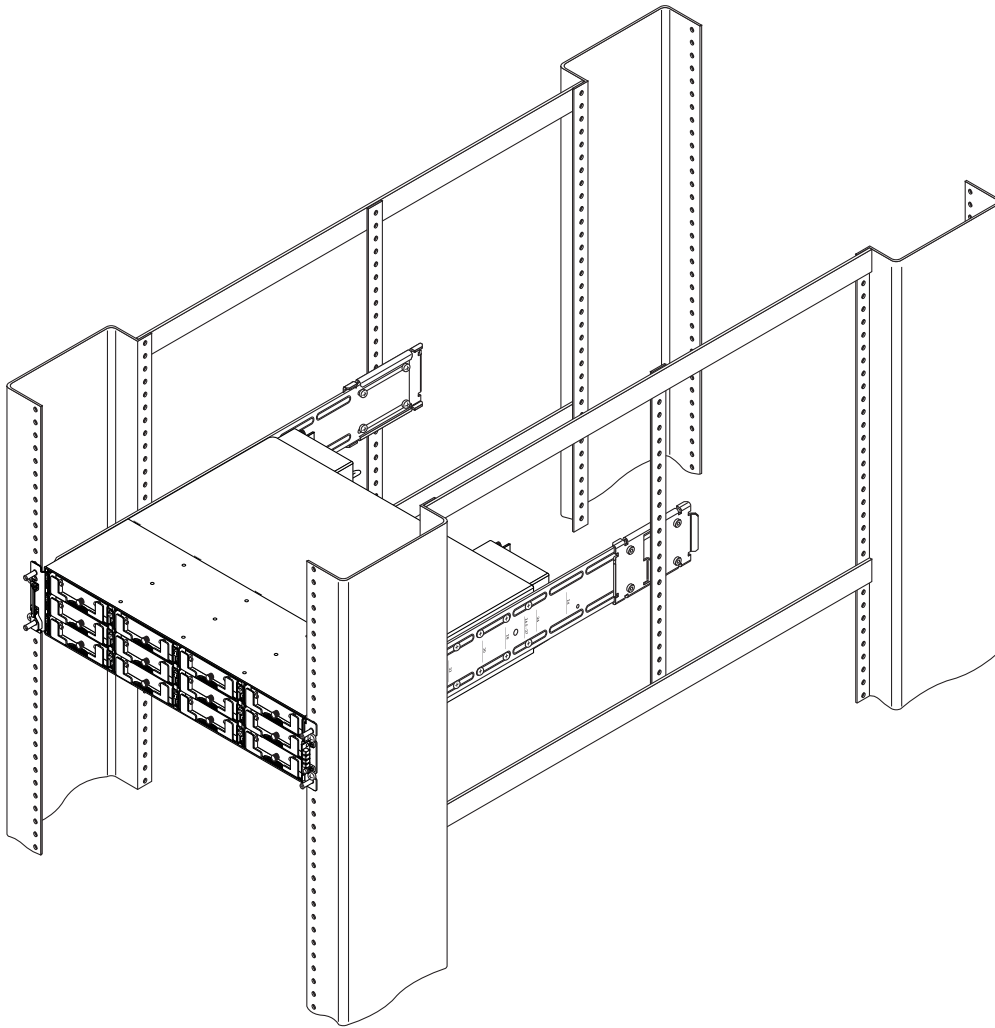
Montage en coffret d'une baie à l'aide des supports du milieu et après retrait des oreilles du châssis et des panneaux - installation terminée
